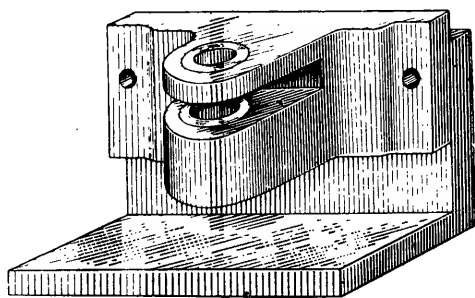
Кондуктор для сверления отверстий под валик в шарнире полоза
